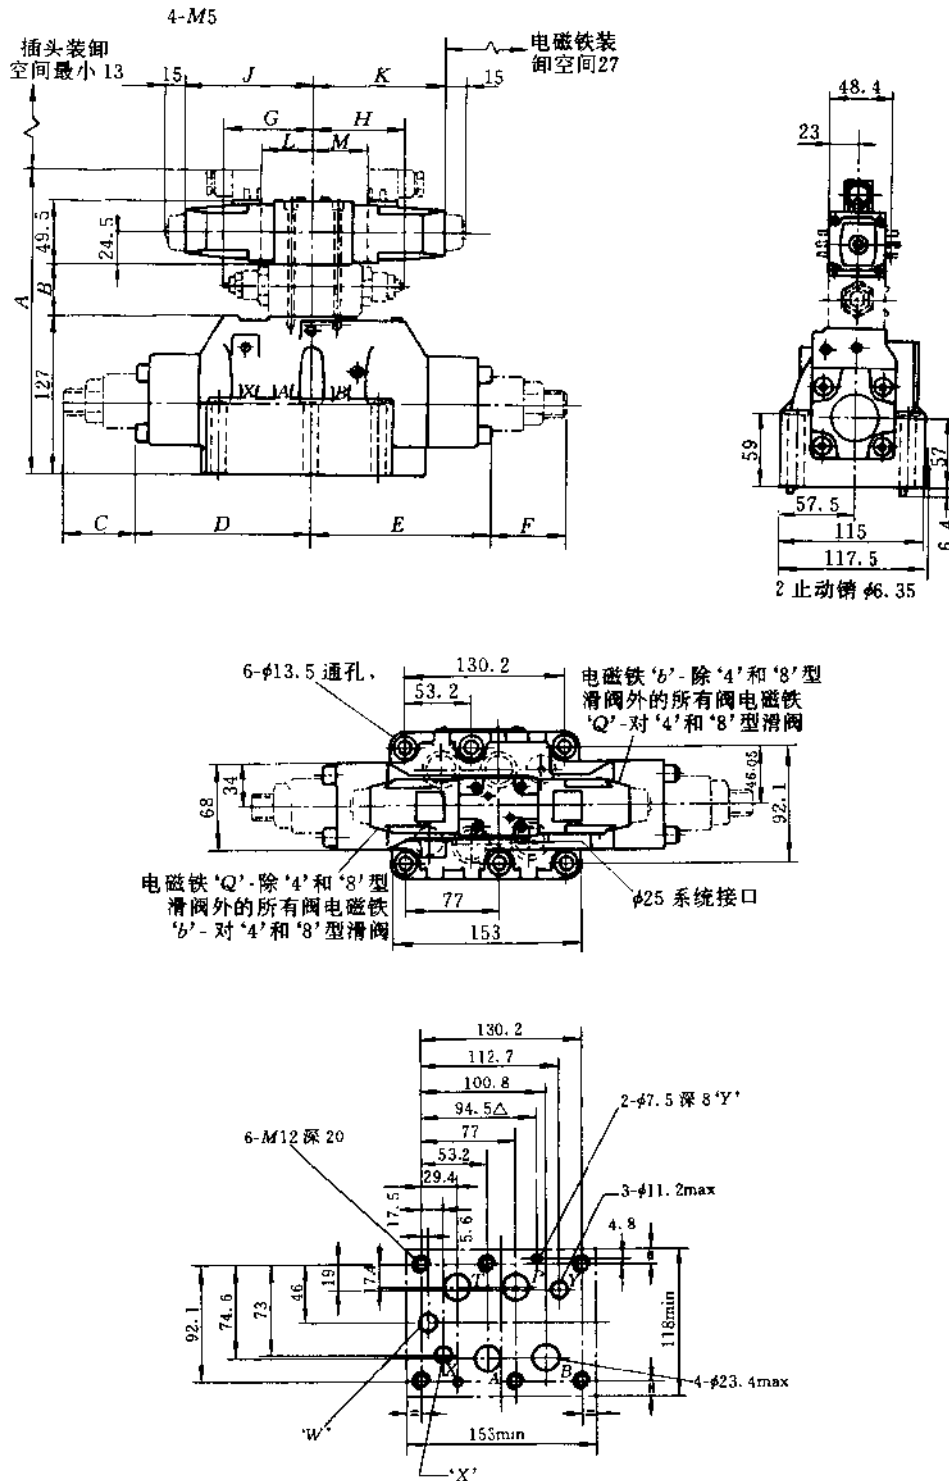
DC5S-H8 型电磁换向阀外形及安装尺寸图
